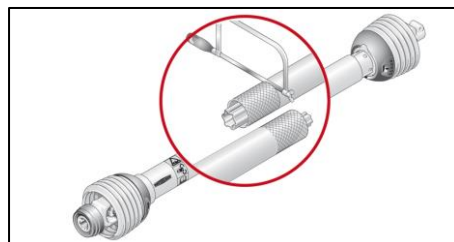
Adapter l'arbre de transmission à joints de cardan
